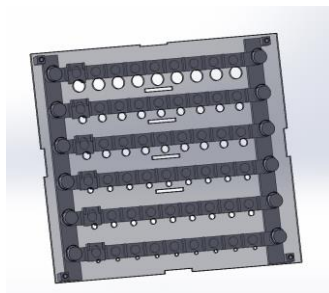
Трехмерная модель передней крышки с пластиковыми деталями
